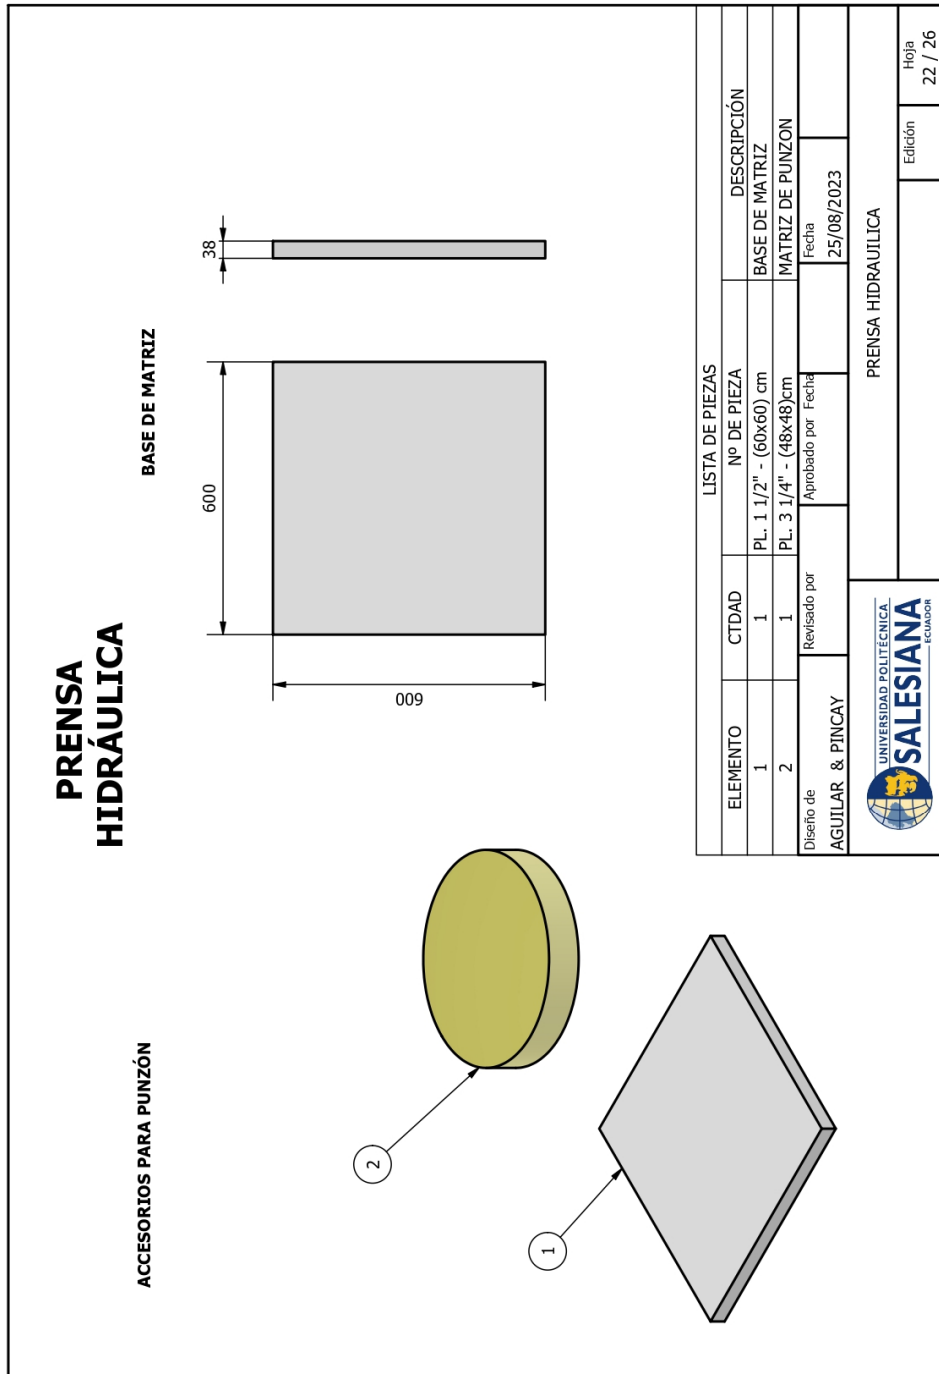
Lámina del las dimensiones de los accesorios para el punzón , por M. Aguilar y E. Pincay, Autodesk Inventor
